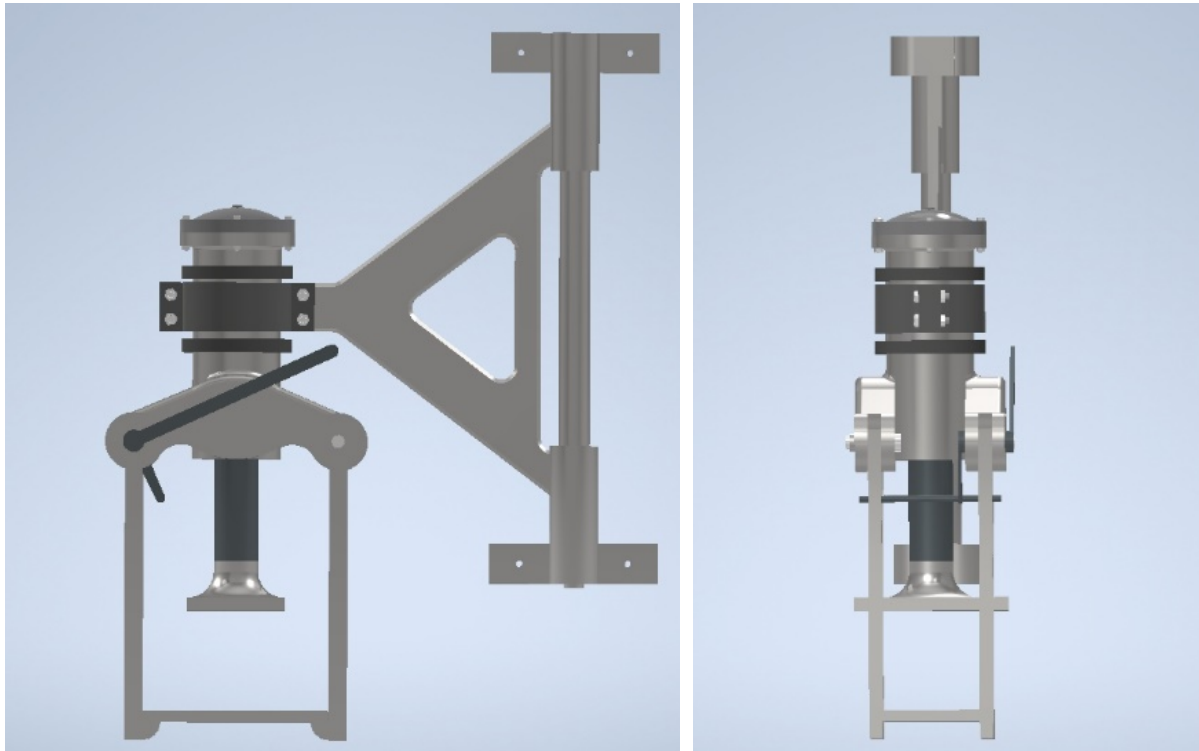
Vistas frontal y lateral del ensamblaje final.
